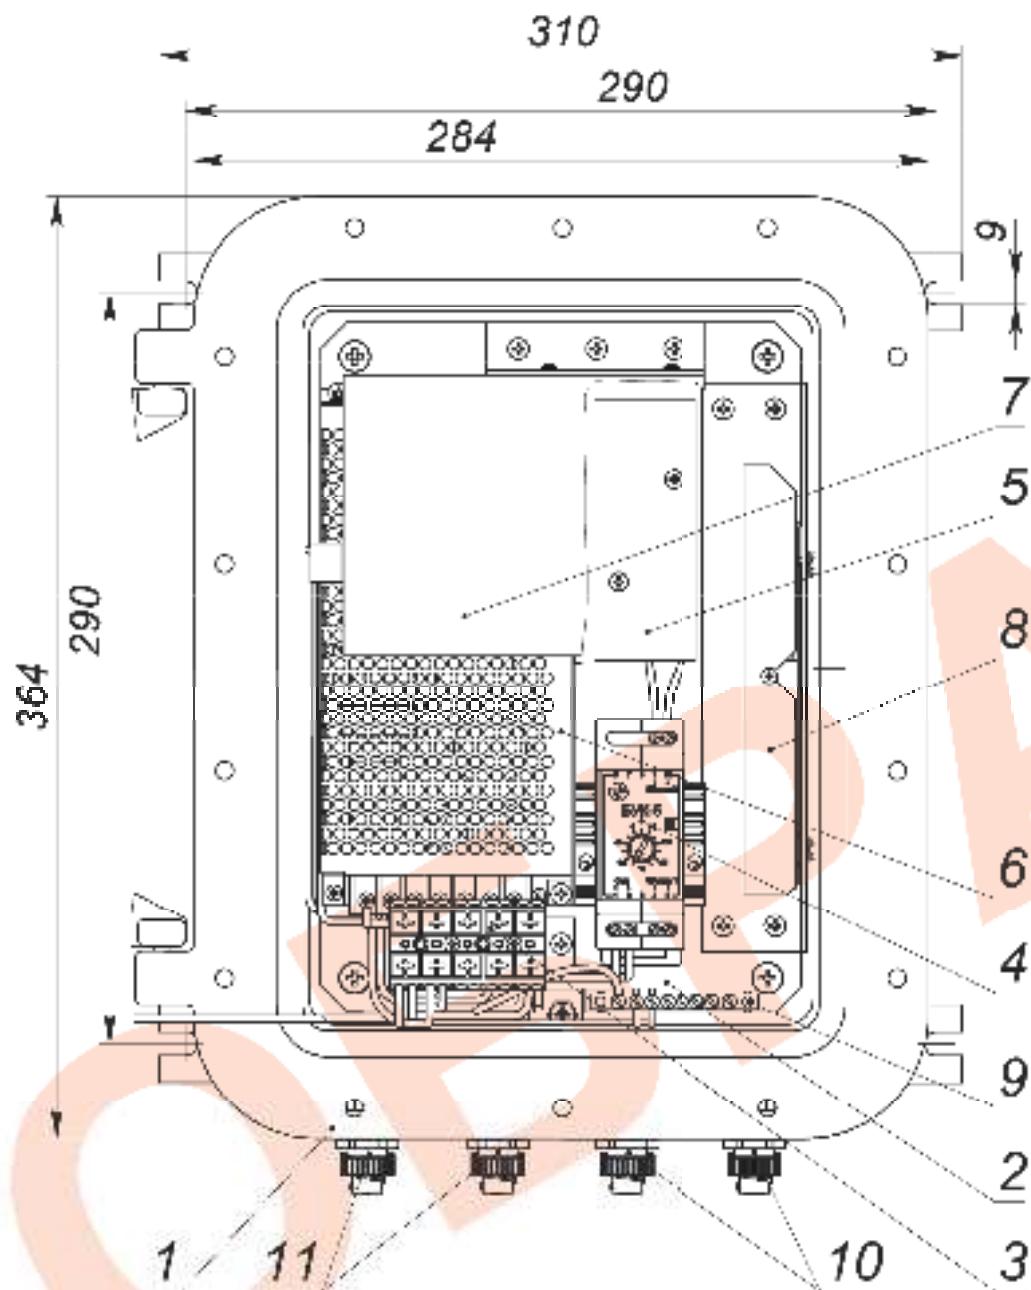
Устройство и габаритно установочные размеры ВУК-ББ-14 PoE+ (крышка не показана)
